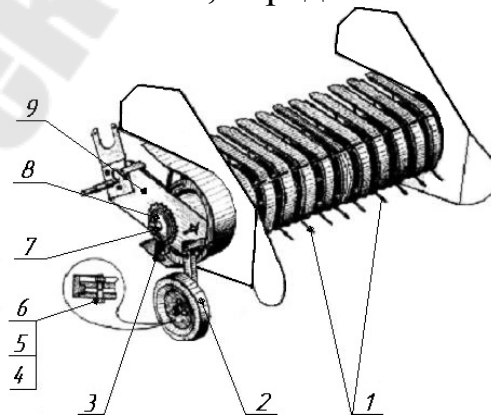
Подборщик: 1 – зубья пружинные; 2 – колесо опорное; 3 – дорожка; 4 – болт; 5 – гайка; 6 – шайба; 7 – вал приводной; 8 – муфта предохранительная; 9 – боковина
